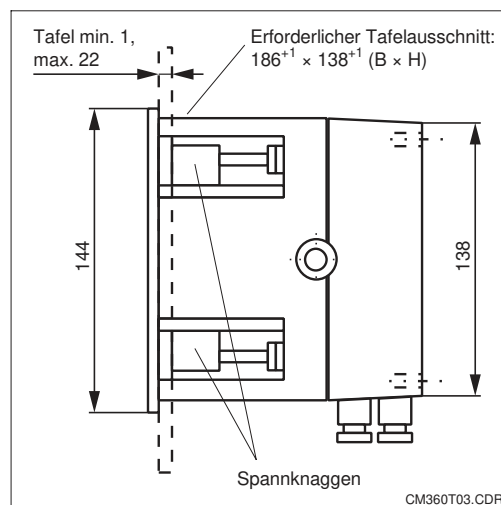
OCM 360, Seitenansicht mit Schalttafelausschnitt
